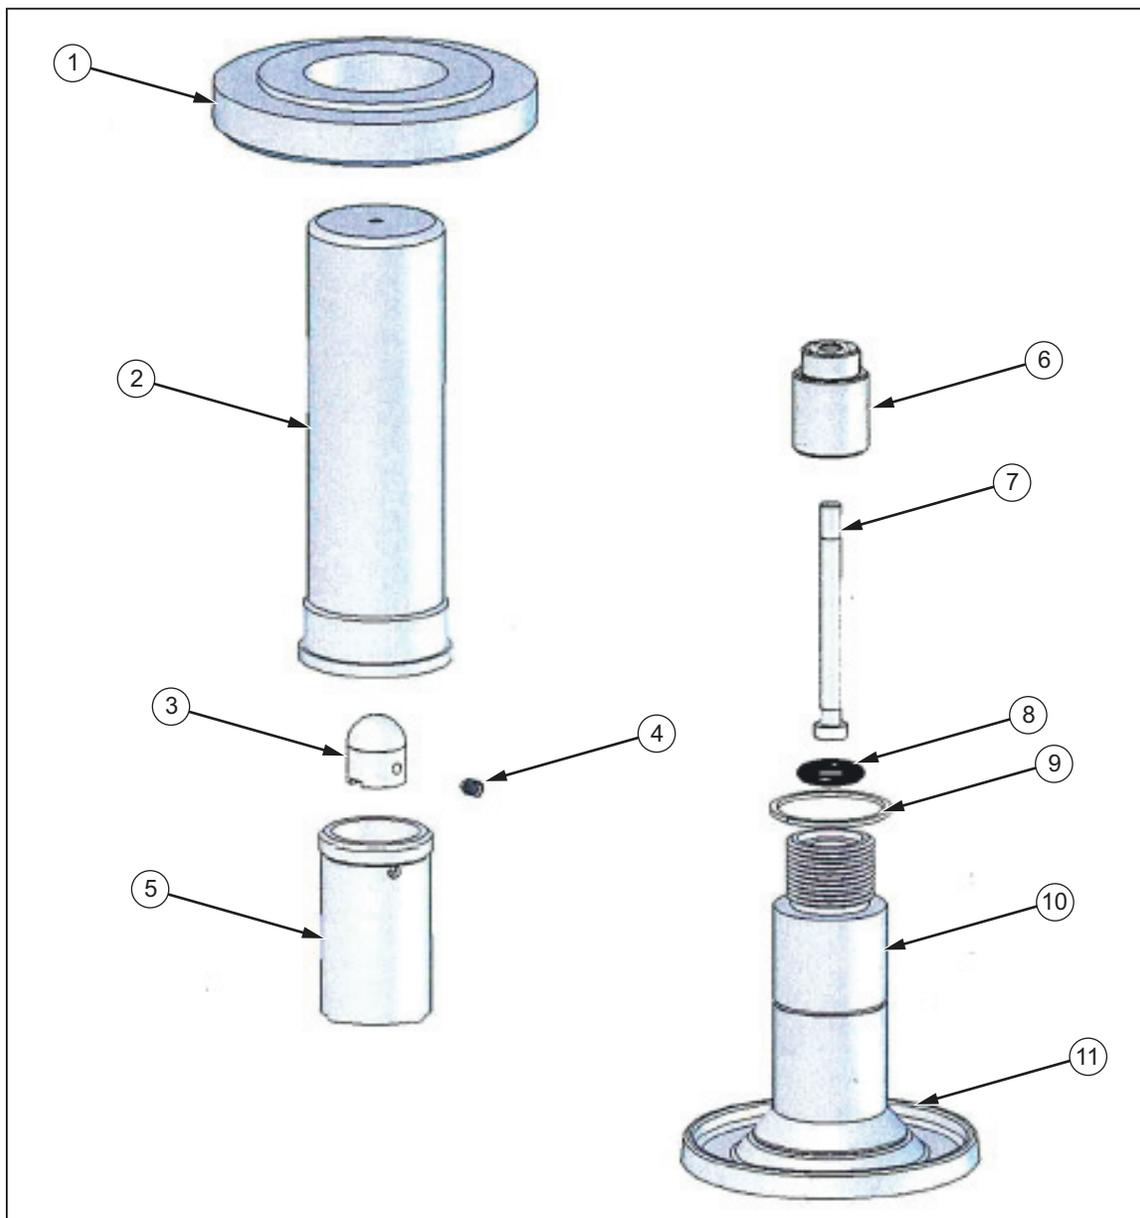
Сборочный чертеж поршневой пары - 5 мм
